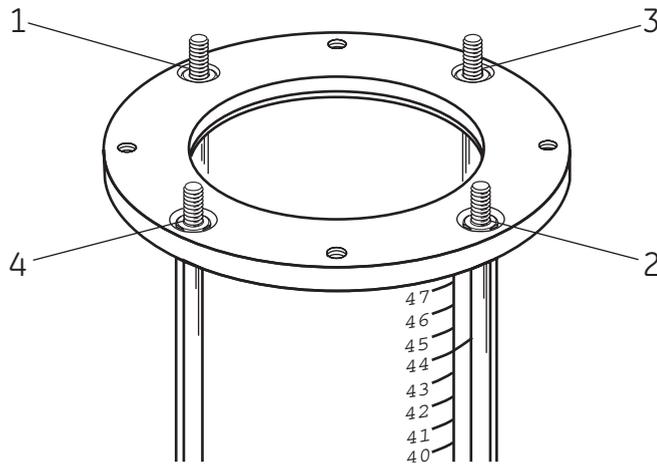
Sequenza di rimozione e di serraggio dei dadi.
